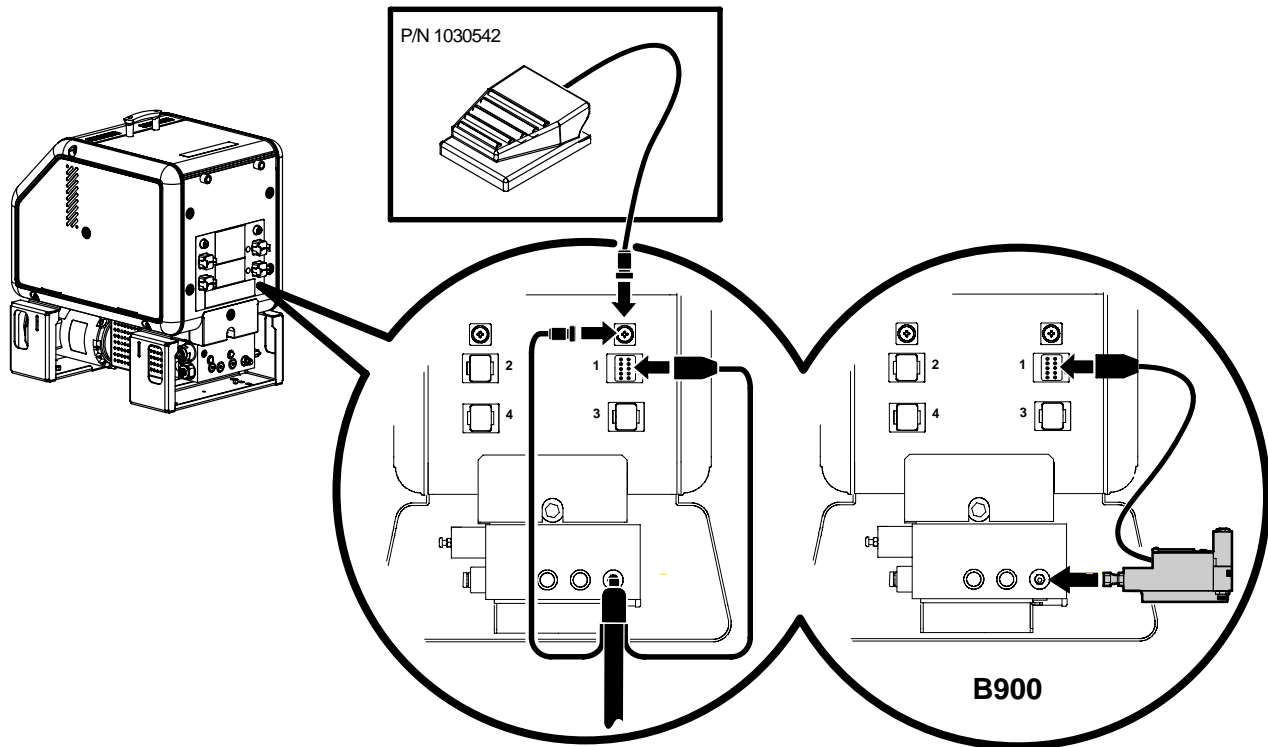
Schlauch für Handpistole mit Schalter, Fußschalter oder elektrischen Auftragskopf B900N anschließen
